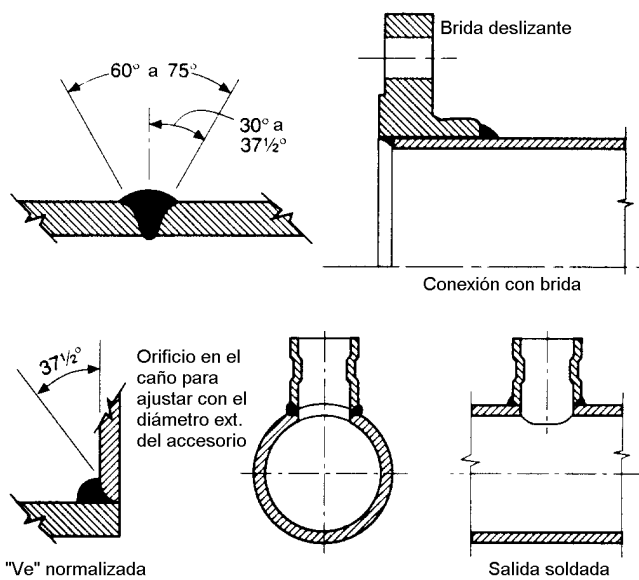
(a) Uniones soldadas aceptables.
